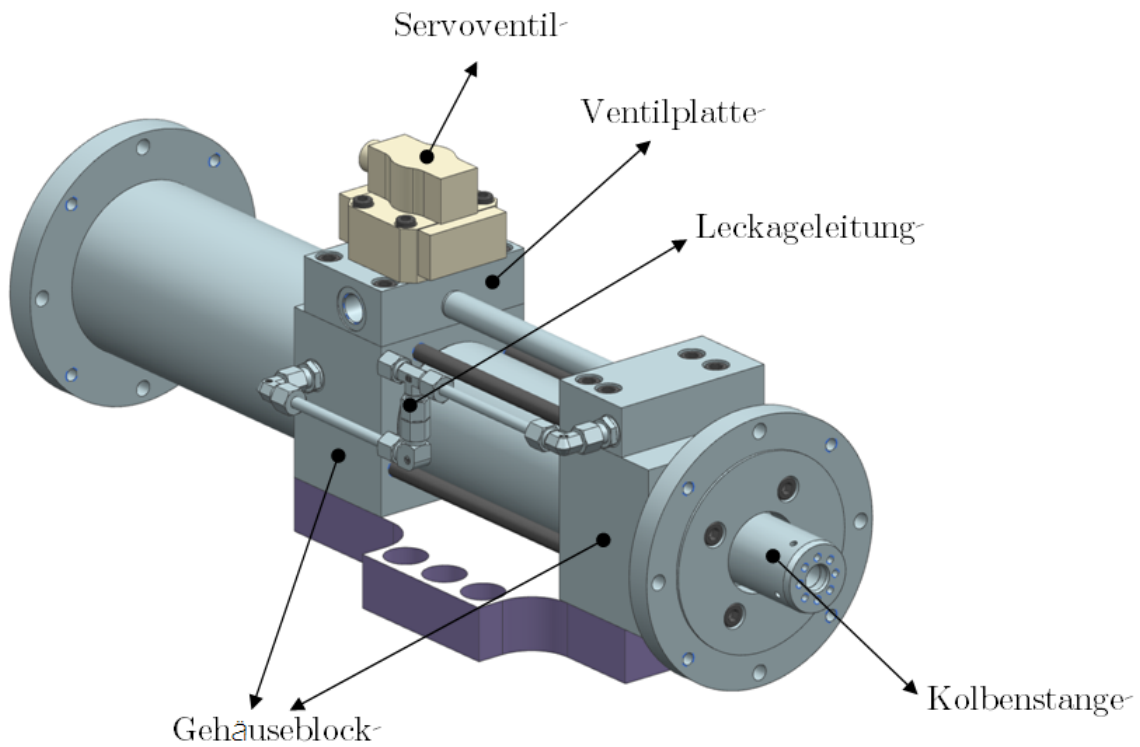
Isometrieansicht des Hydraulikzylinders
